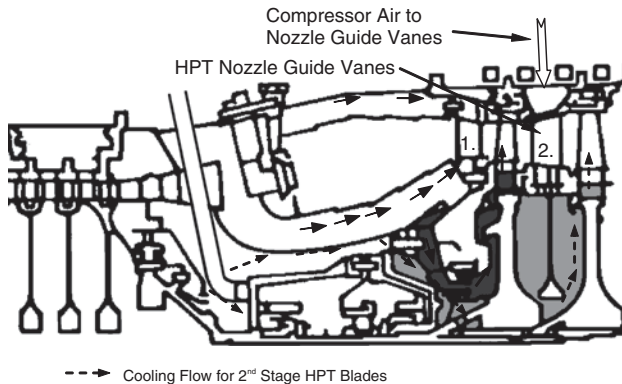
Kühlluftversorgung der Hochdruckturbinen in einem V2500
